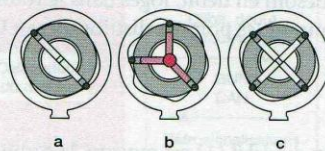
Pistons radiaux possibles dans un rotor d'une pompe Bosch « VP44 »
